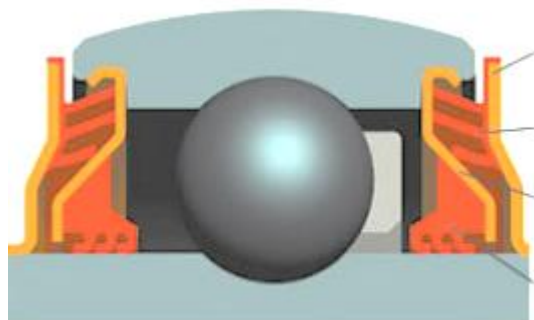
Конструкція системи ущільнювача X-SHIELD-6 підшипника HARP AGRO
